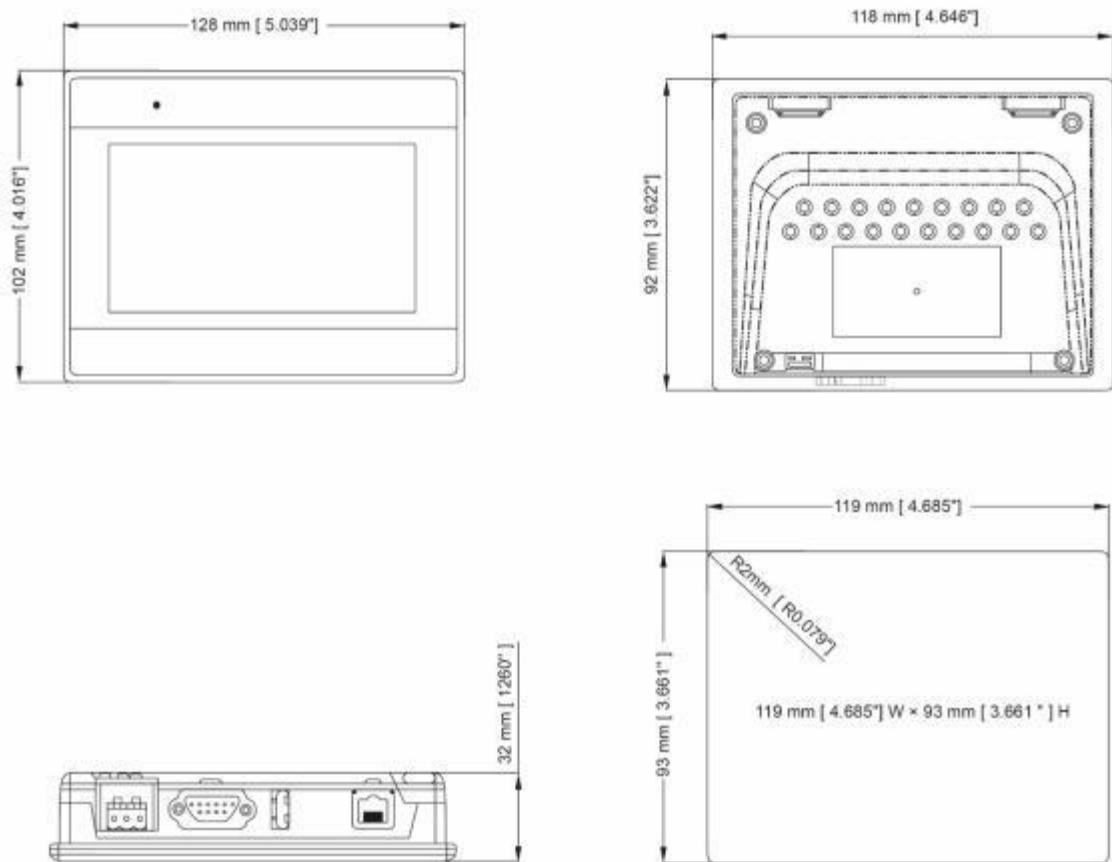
Габаритные и установочные размеры панели VG4 (4,3")
